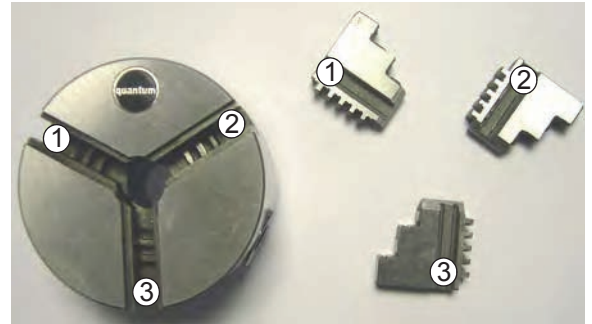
Mandrin à 3 mors / Mors de serrage
